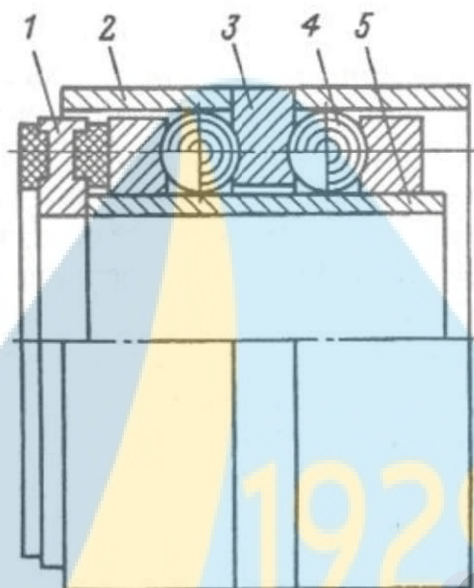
Ступінь багаторядного упорного підшипника кочення з гумовим компенсатором типу ІШШО
